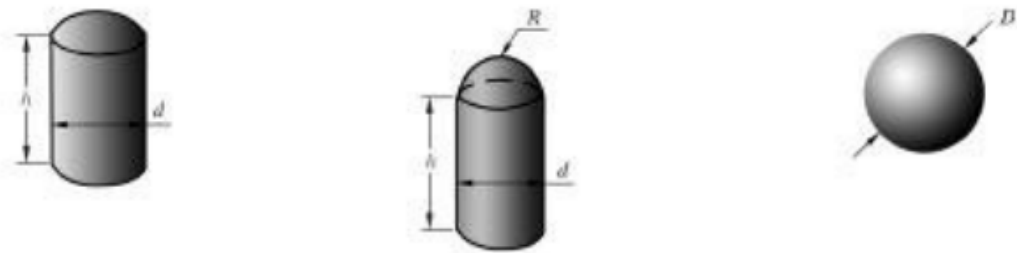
端面为平面的圆柱形销 图 F.3 端面为球面的圆柱形销 图 F.4 滚动轴承钢球替代销试样
